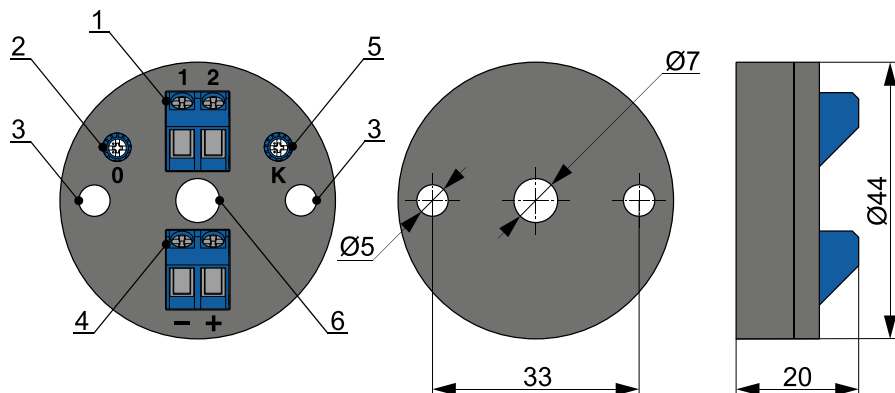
Габаритные размеры преобразователя с корпусом исполнения 01
